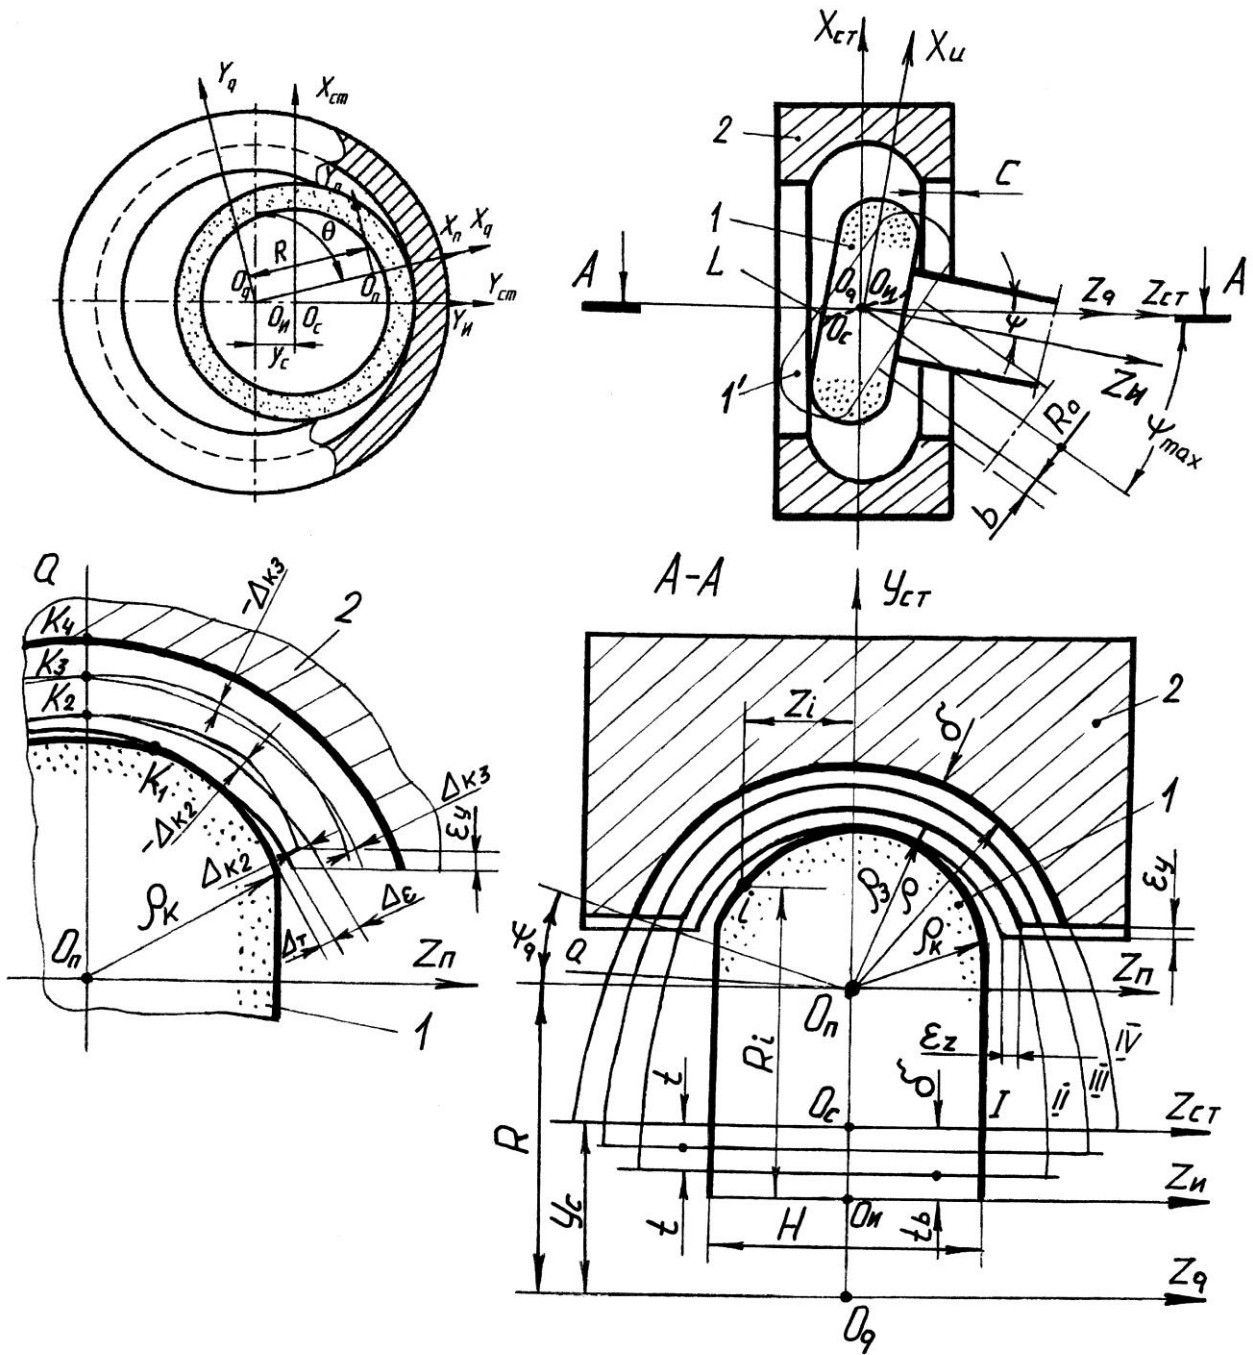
Схема шліфування внутрішніх торових поверхонь зі схрещеними осями круга і зовнішнього кільця шарикопідшипника
